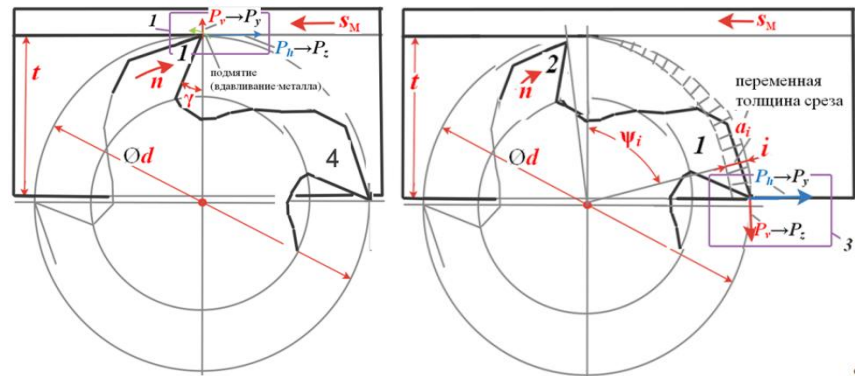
Схема направления составляющих силы резания при несимметричном встречном концевом фрезеровании четырёхзубой фрезой при глубине фрезерования $t = d/2 - 0,2$ мм: а – при врезании зуба № 1; б – при выходе зуба № 1 из контакта с заготовкой. Наибольшая толщина среза при выходе зуба из контакта $a_{\max} \approx 2 \times s_z \times \sqrt{t/D}$
